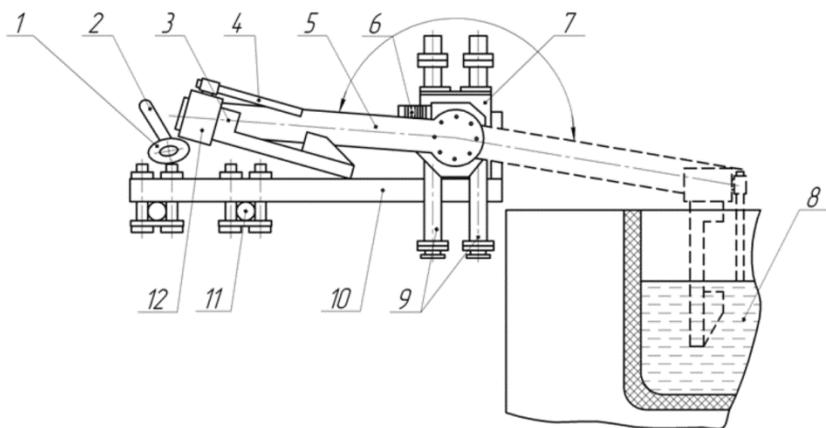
Автооператор-заливщик для машины литья под давлением – базовый образец агрегатной гаммы ЛМЗ (Украина): *1* – заливочное окно; *2* – направляющий лоток; *3* – ковш; *4* – датчик; *5* – рычаг; *6* – регулировочный винт; *7* – поворотный механизм; *8* – тигель с металлом; *9* – гидроцилиндры; *10* – кронштейн; *11* – машина литья под давлением; *12* – хомут
